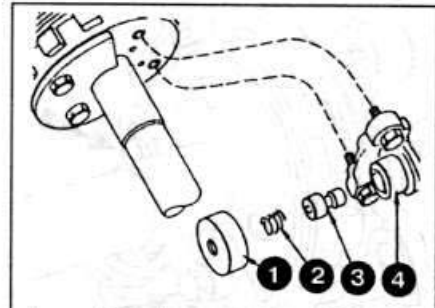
Детали центробежного регулятора давления масла: 1 — грузик; 2 — пружина клапана; 3 — клапан; 4 — корпус
